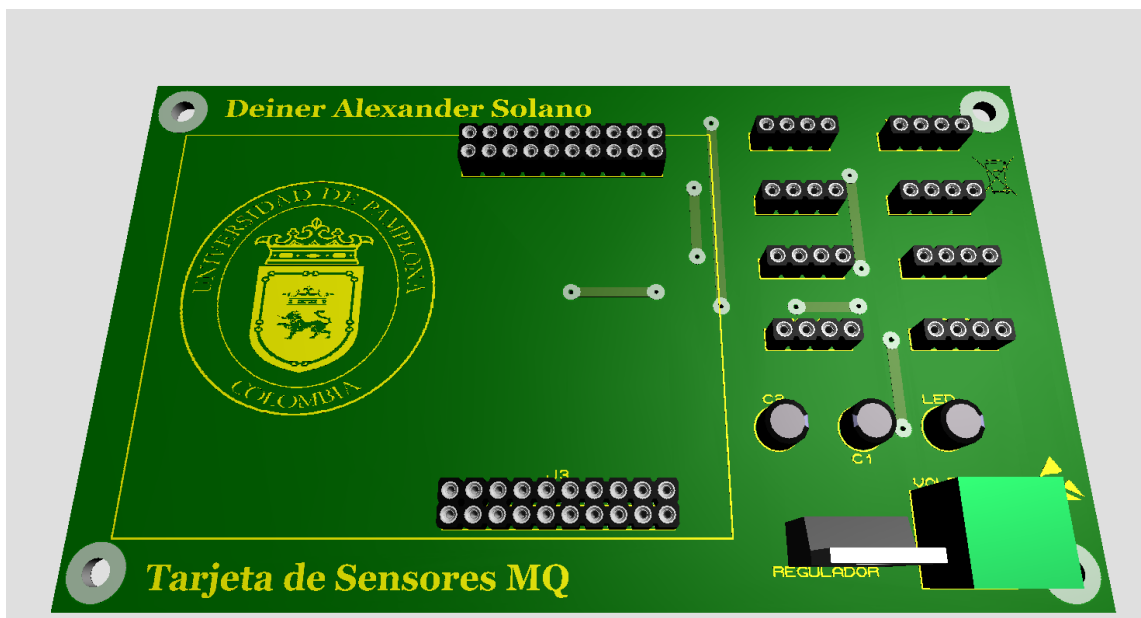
Diseño 3D de la Tarjeta de Sensores MQ
